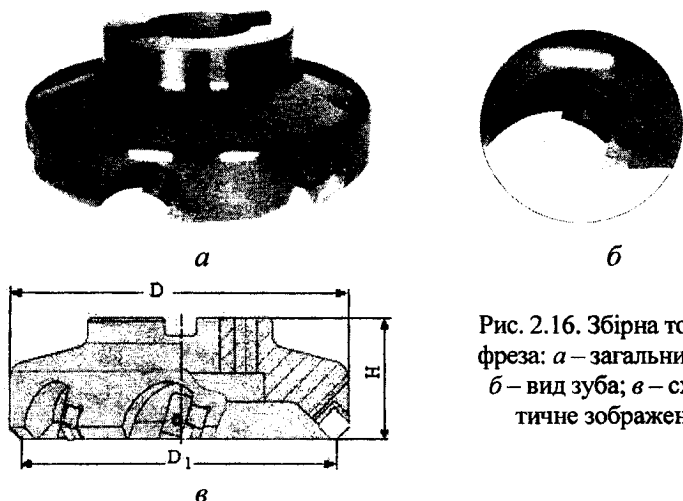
Збірна торцева фреза: а – загальний вид; б – вид зуба; в – схематичне зображення
